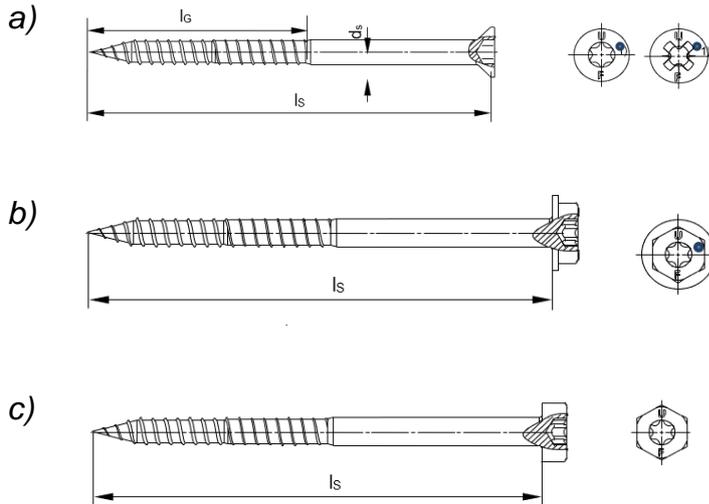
Technische Zeichnungen der Spezialschrauben: a) Senkkopfschraube, b) Sechskantschraube mit angepresster Unterlegscheibe und c) Sechskantschraube.
